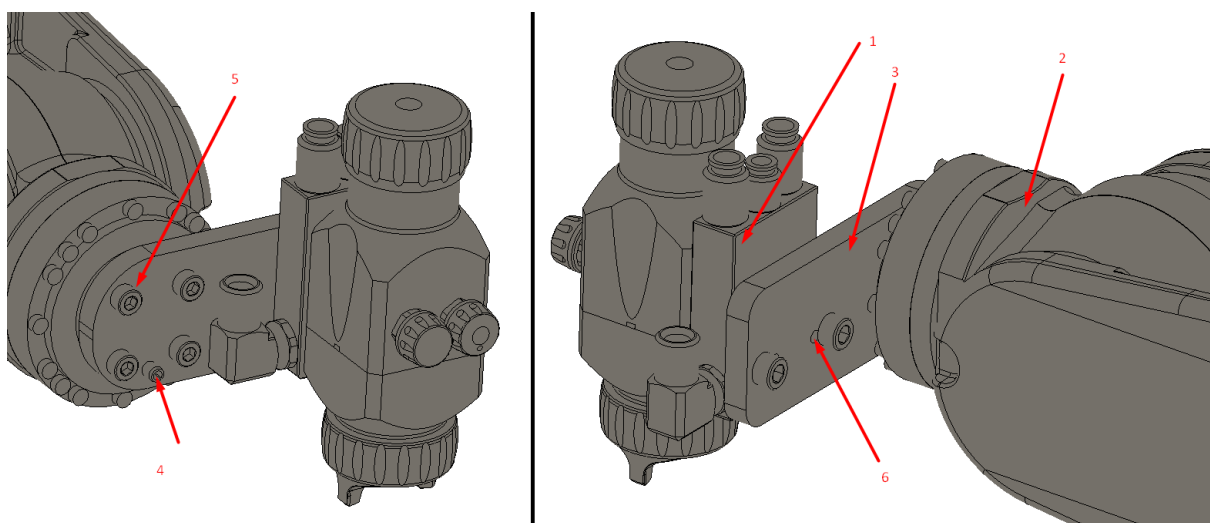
Nákres stříkácí pistole Wagner Ga 1030 bez adaptéru a s adaptérem [50]
